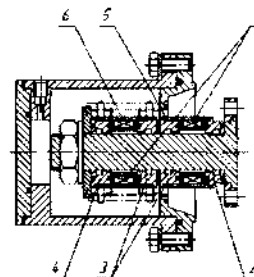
Сборочный чертеж гидроцилиндра МР модуля
